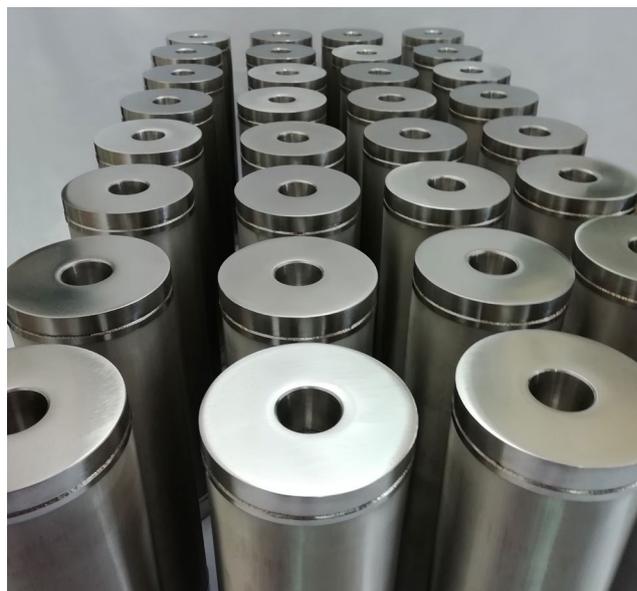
Фильтры ЭФП-222 цельнометаллической конструкции
